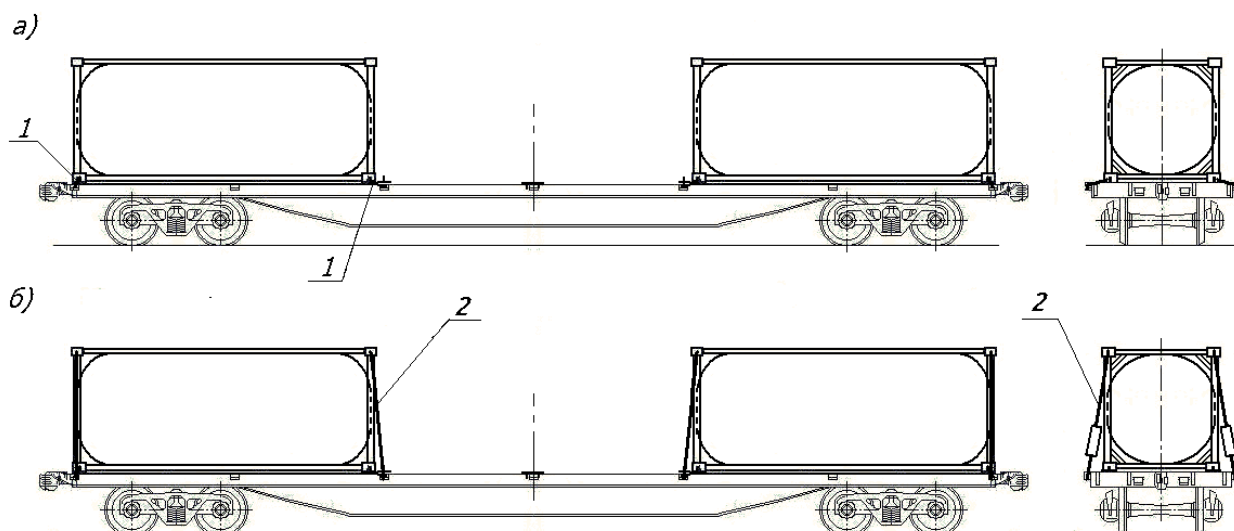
Дополнительное крепление контейнеро-цистерн на платформе для крупнотоннажных контейнеров:
